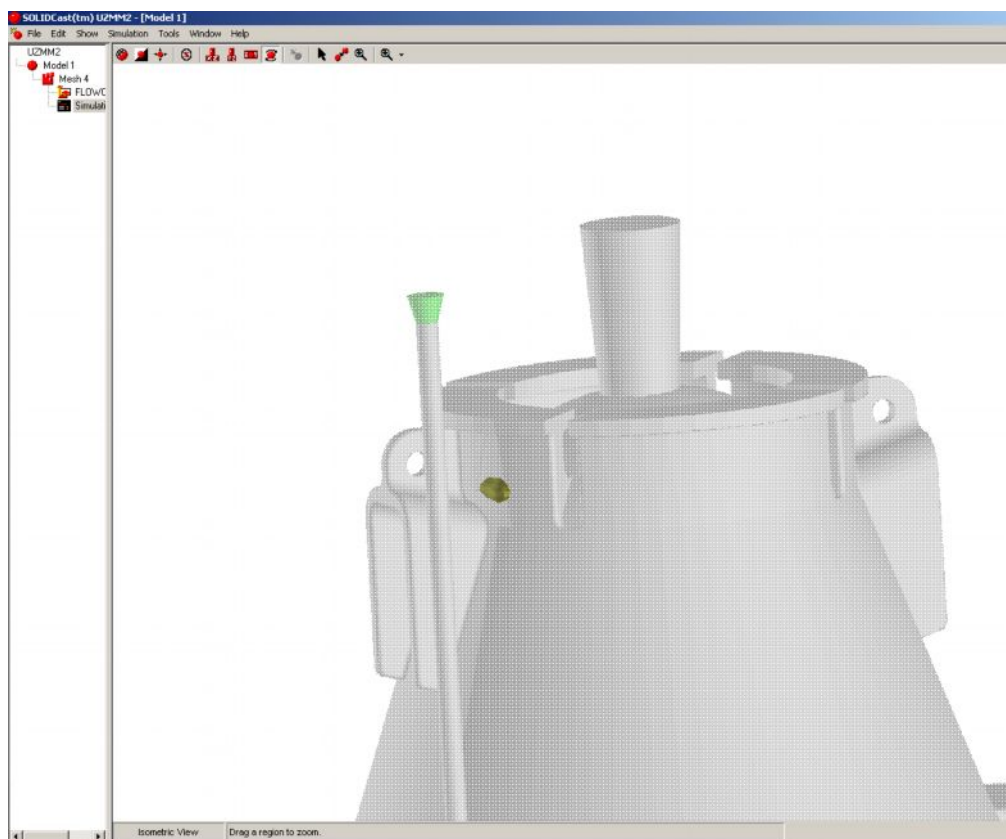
Усадочные дефекты в отливке “Чаша”
